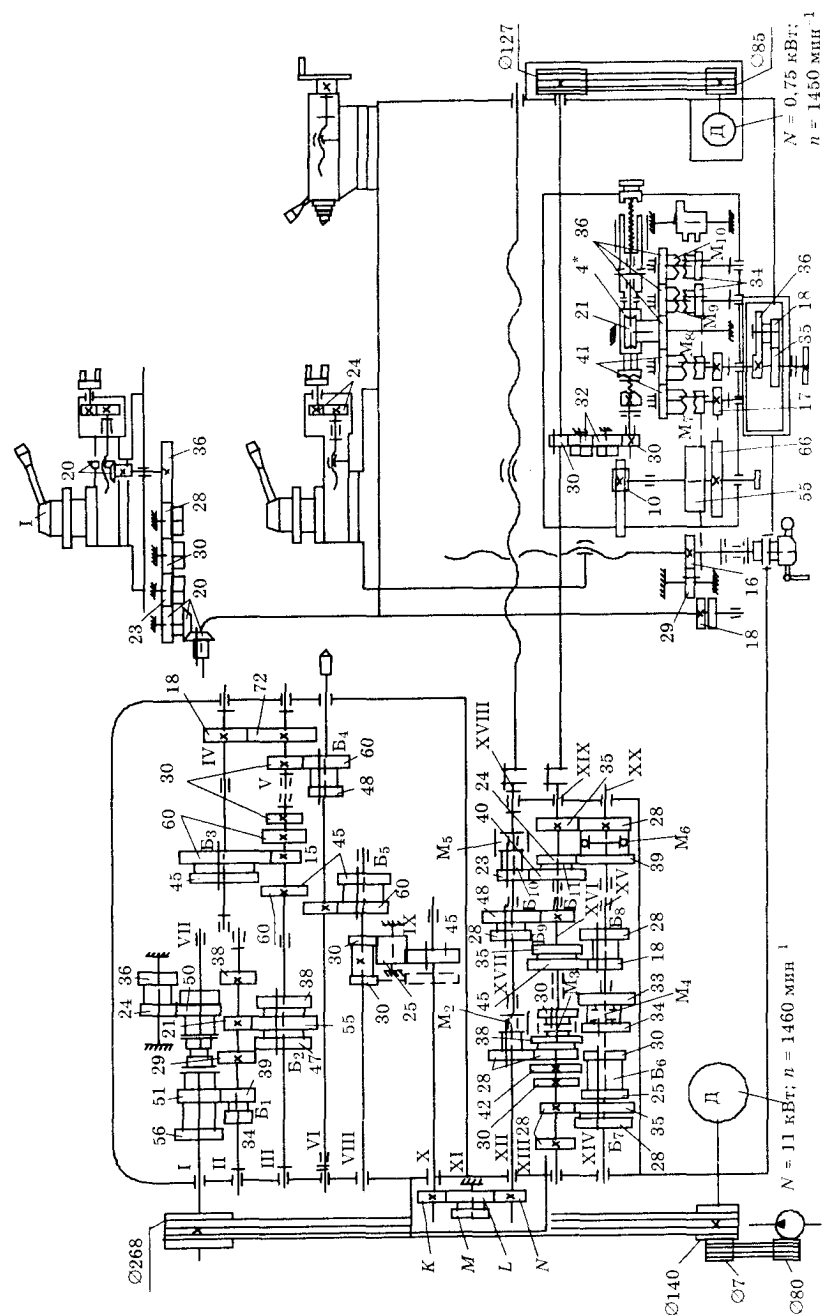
Кинематическая схема токарно-винторезного станка 16K20
